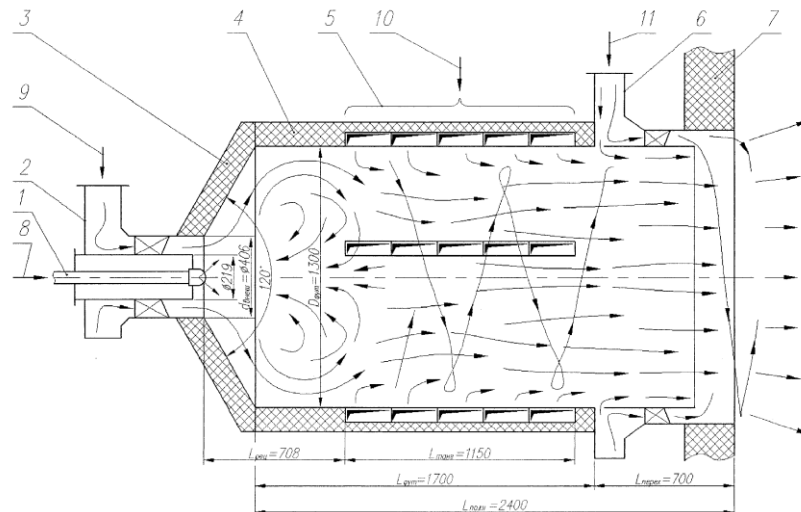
Конструкция ЦП тепловой мощностью 12 МВт: 1— пневмомеханическая форсунка; 2-вихревая горелка; 3-передняя коническая стенка; 4-цилиндрический футеровочный корпус; 5-сопла тангенсального воздуха; 6-короб третичного воздуха; 7-стенка котла; 8-подача ТД ВУС; 9-подача аксиального воздуха; 10-подача тангенциального воздуха; 11-подача третичного воздуха
